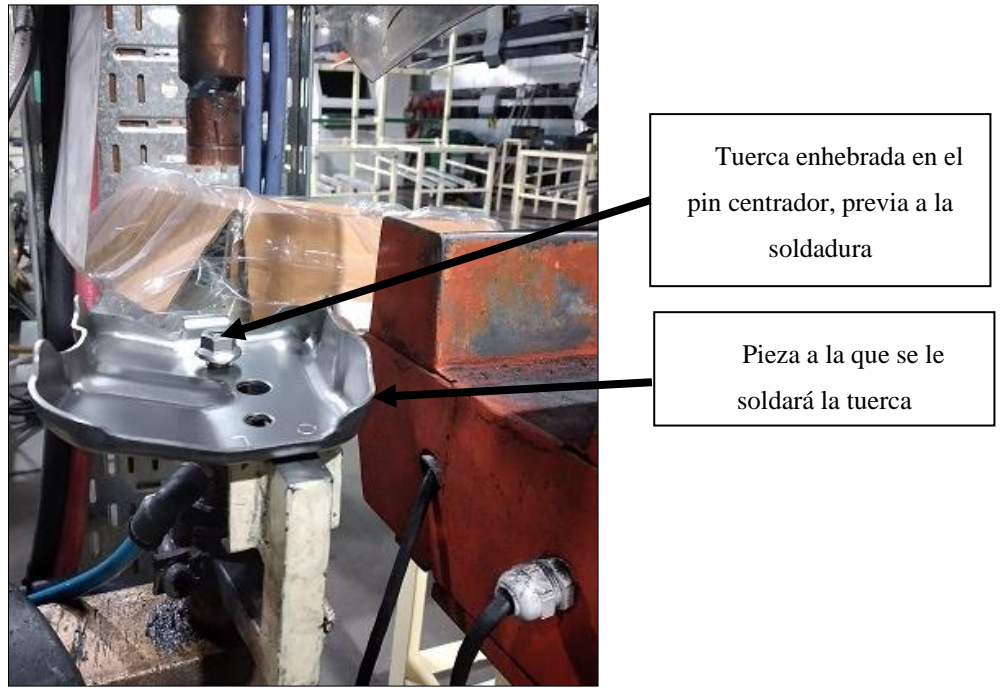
Vista de la pieza ubicada en la máquina soldadora, con la tuerca enhebrada en el pin centrador.
